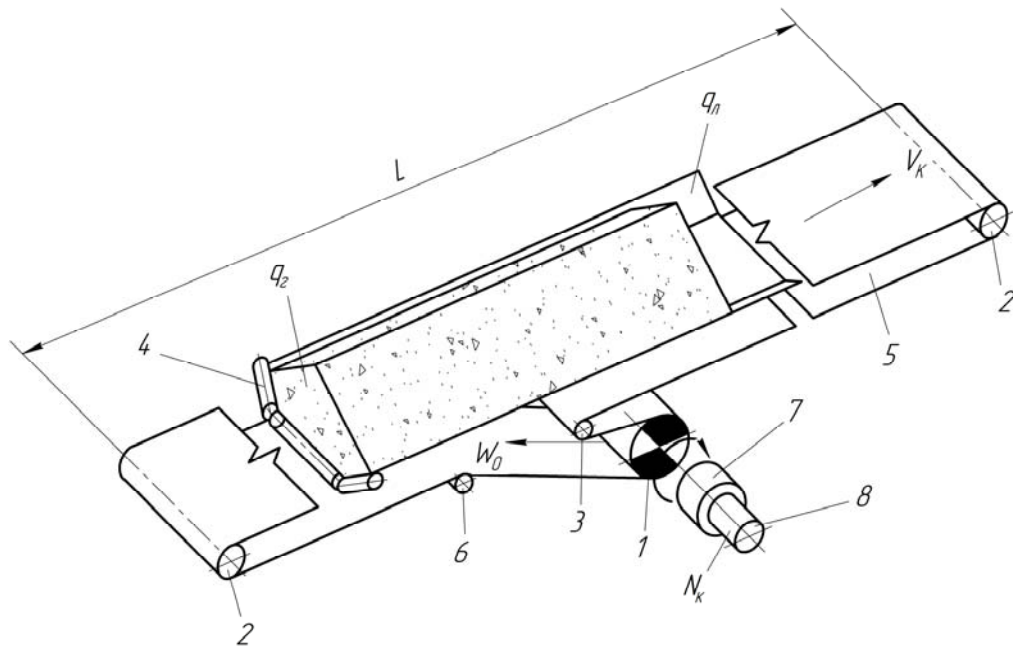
Принципиальная схема разгрузочного и погрузочного конвейеров карьерного комбайна: 1 - приводной барабан; 2 - концевые барабаны; 3 - натяжной барабан; 4 - роликоопора; 5 - конвейерная лента; 6 - отклоняющий барабан; 7 - редуктор; 8 - гидромотор
